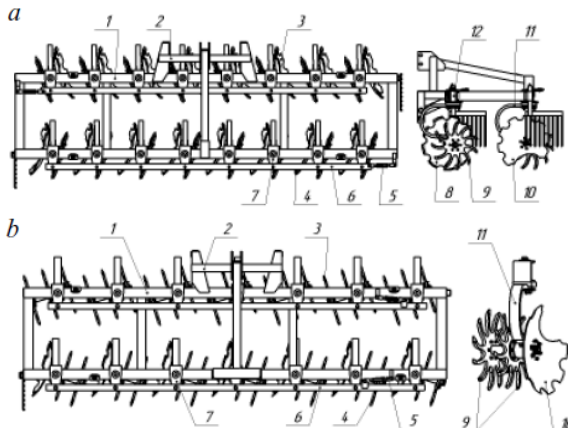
Бороны для противоэрозионной обработки почвы, вид сверху:
